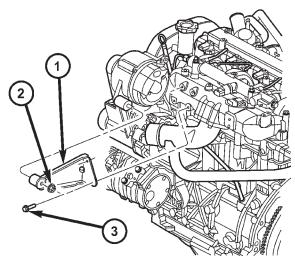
GENERADOR - MOTOR 2.5 DIESEL
